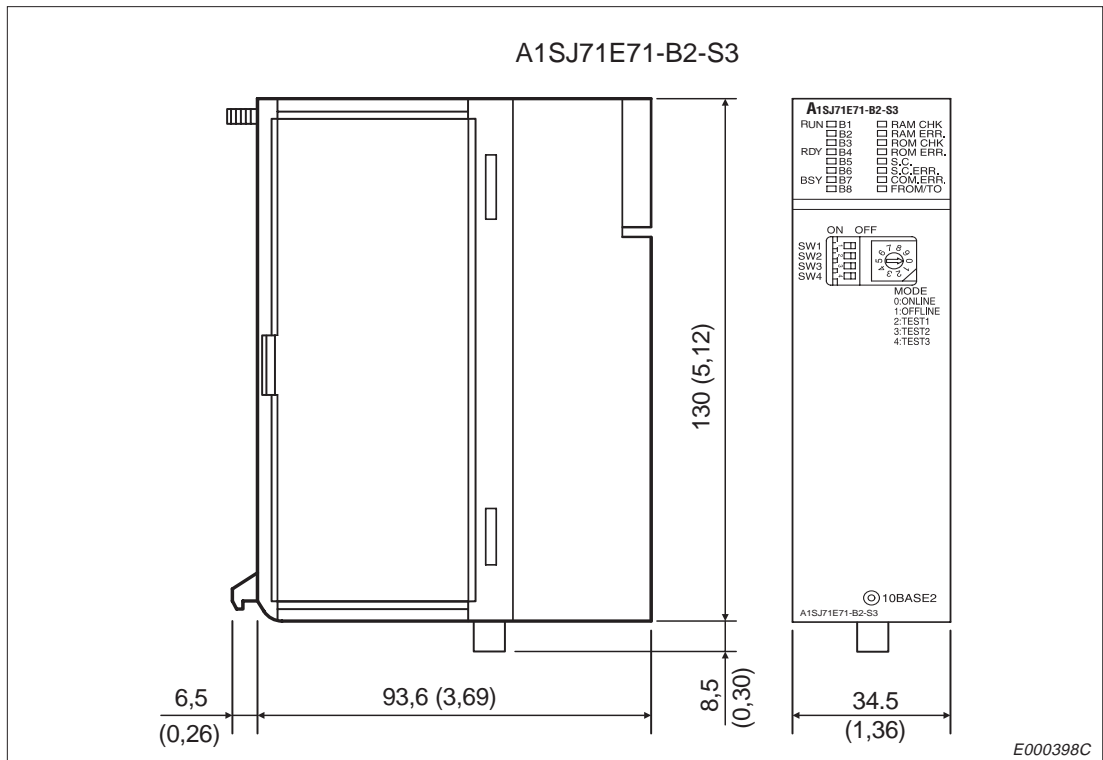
Gehäuseabmessungen des A1SJ71E71-B2-S3
